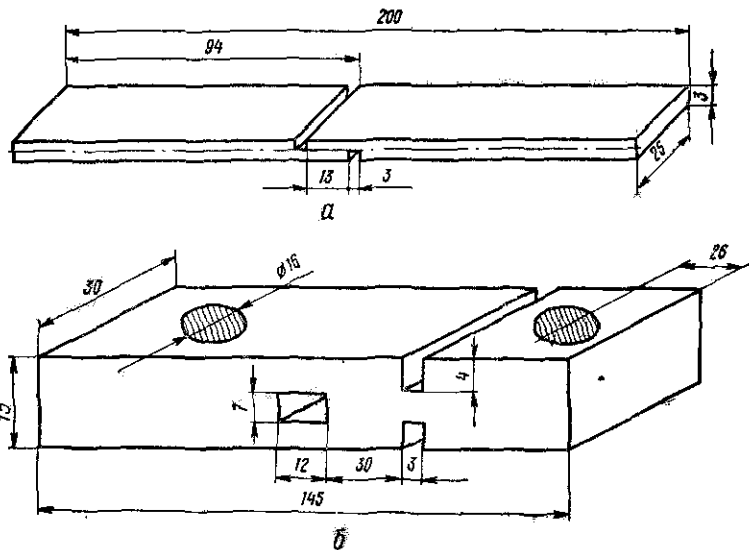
Образцы для испытаний на межслойный сдвиг:
